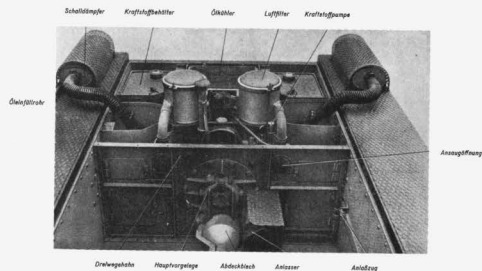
Fahrgestell, innen, in Richtung des Motorraumes
